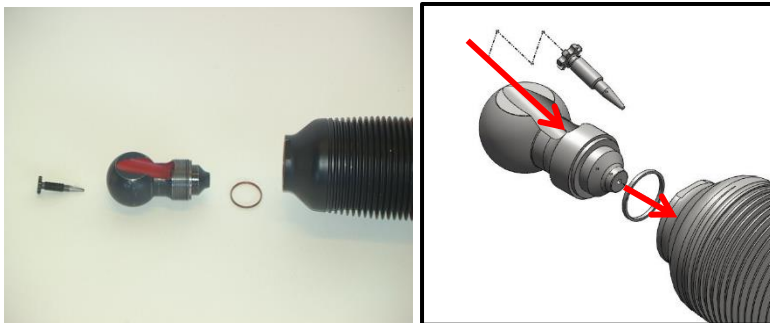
Parte posterior do conjunto Tubo. (à esq.) Percutor, culatra, anel de vedação e tubo alinhados; e (à dir.) vista explodida desses componentes
